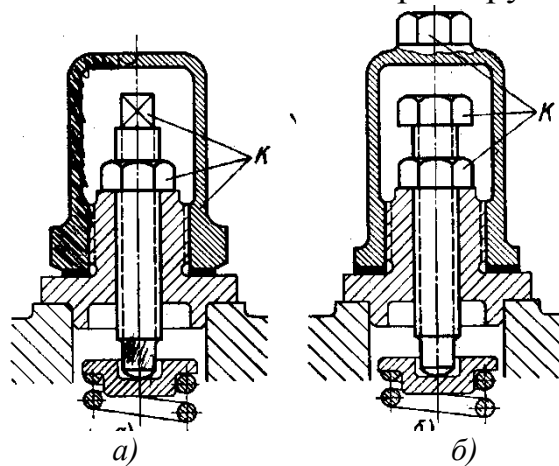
Вузол редукційного клапана (К – поверхні під ключ):
